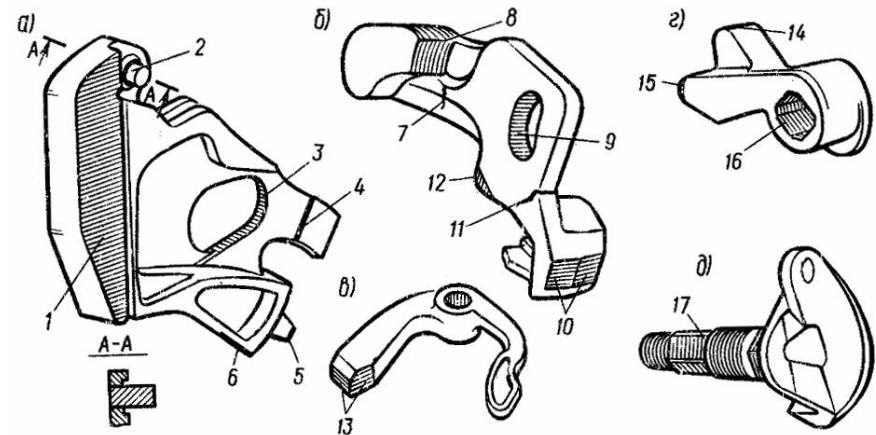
Зоны износов и повреждений деталей механизма сцепления: а – замок; б – замкодержатель; в – предохранитель замка; г – подъемник; д – валик подъемника; 1, 3, 5, 6 – изношенные поверхности замка; 2 – излом шипа; 4 – излом сигнального отростка; 7, 11 – трещины замкодержателя; 8, 9, 10, 12 – изношенные поверхности замкодержателя; 13 – изношенная поверхность предохранителя; 14, 15, 16 – изношенные поверхности подъемника; 17 – изношенные поверхности валика подъемника
